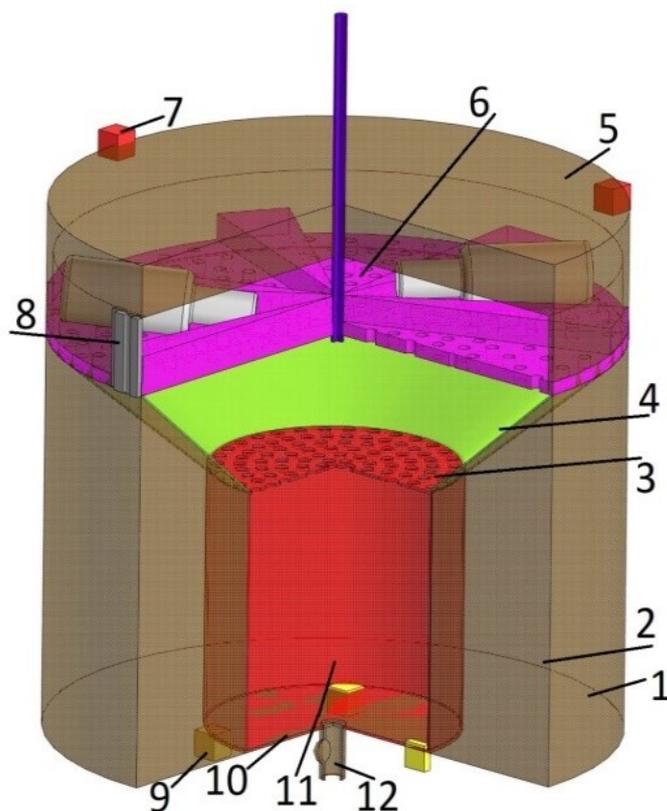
СВЧ-размораживатель молозива животных с соосно расположенными тороидальным и цилиндрическим резонаторами
